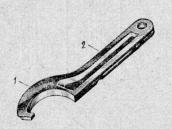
1* — головка; 2 — корпус; 3 — вороток
